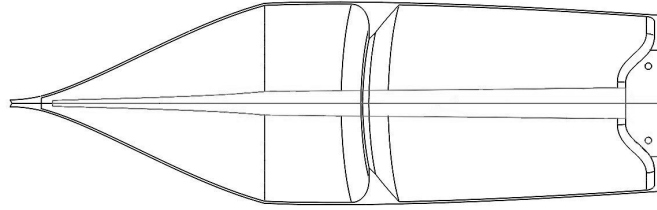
Vista superiore della sezione dell'elemento poppiero fusoliera
